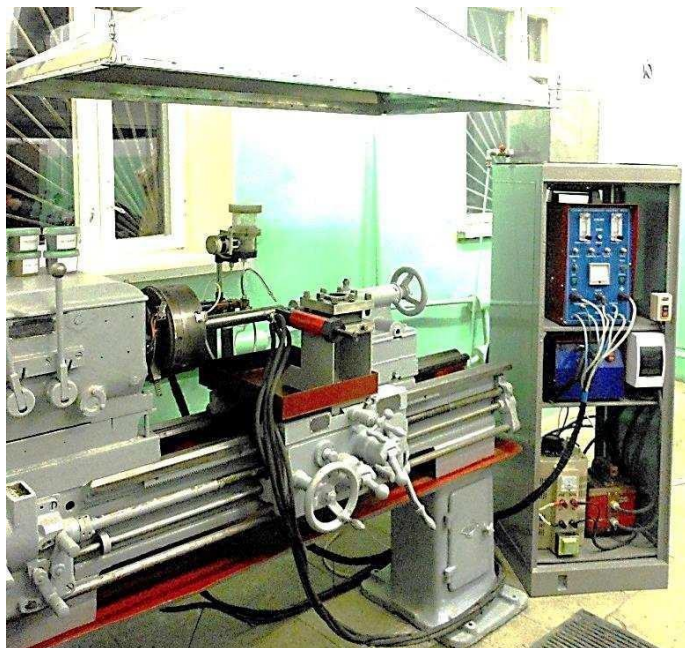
Зовнішній вигляд устаткування для плазмового наплавлення деталей обертання
